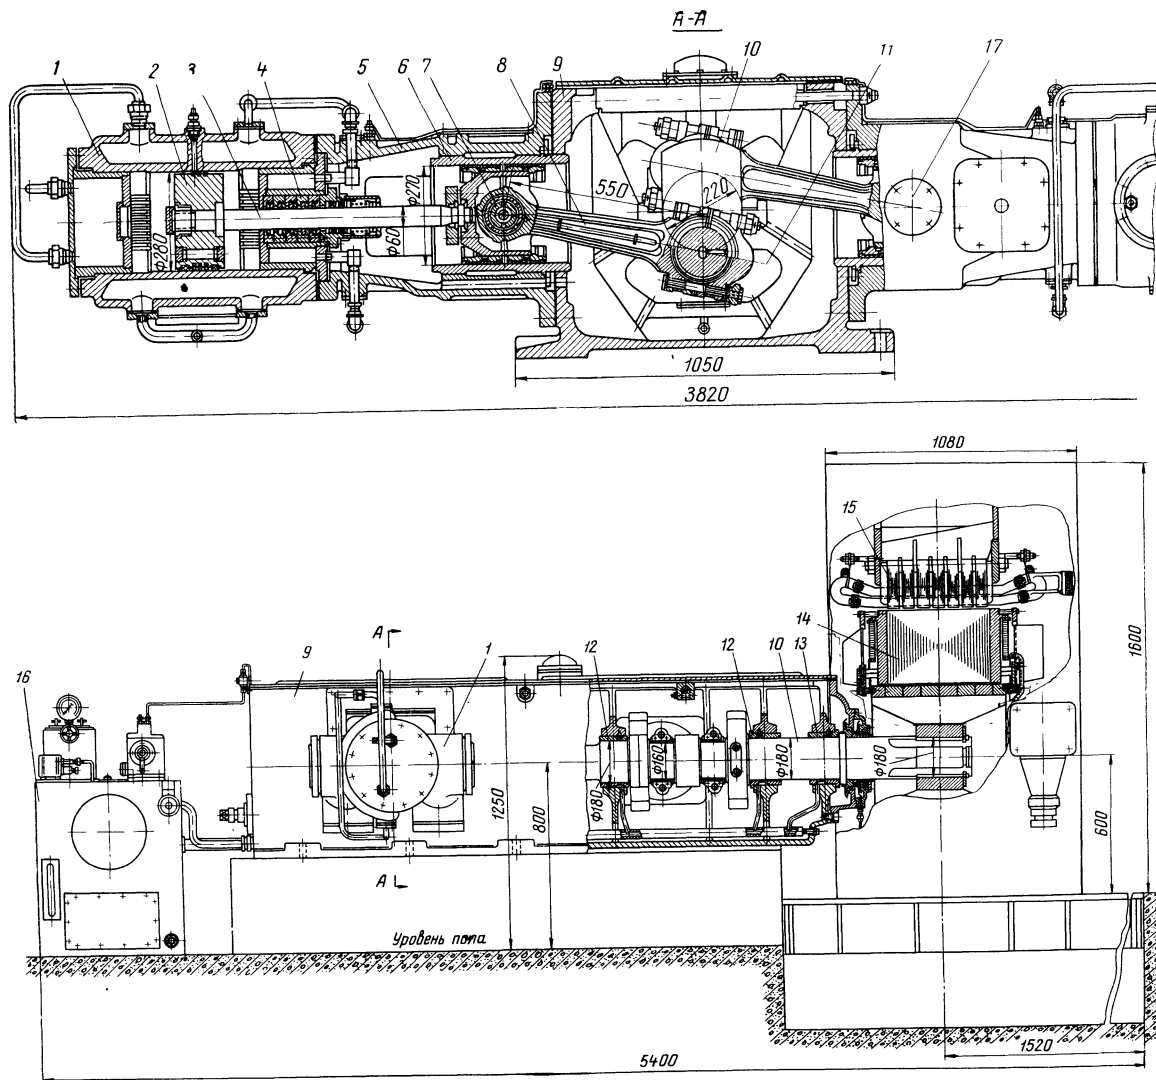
Поперечный и продольный разрезы компрессора АО 1200:
